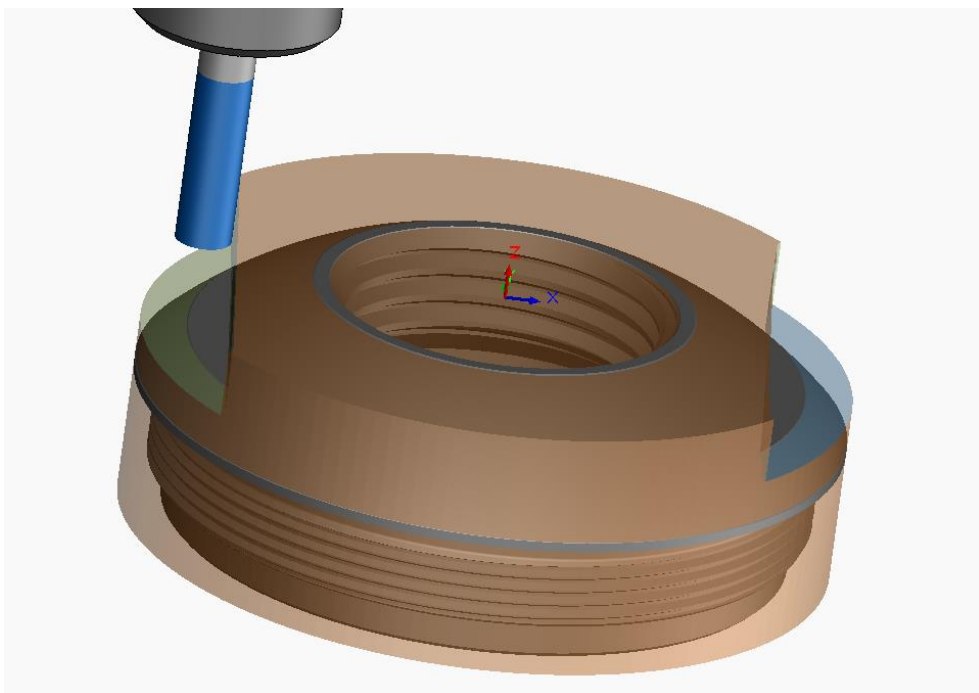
Фрезерування лисок під ключ на вертикально фрезерному верстаті
